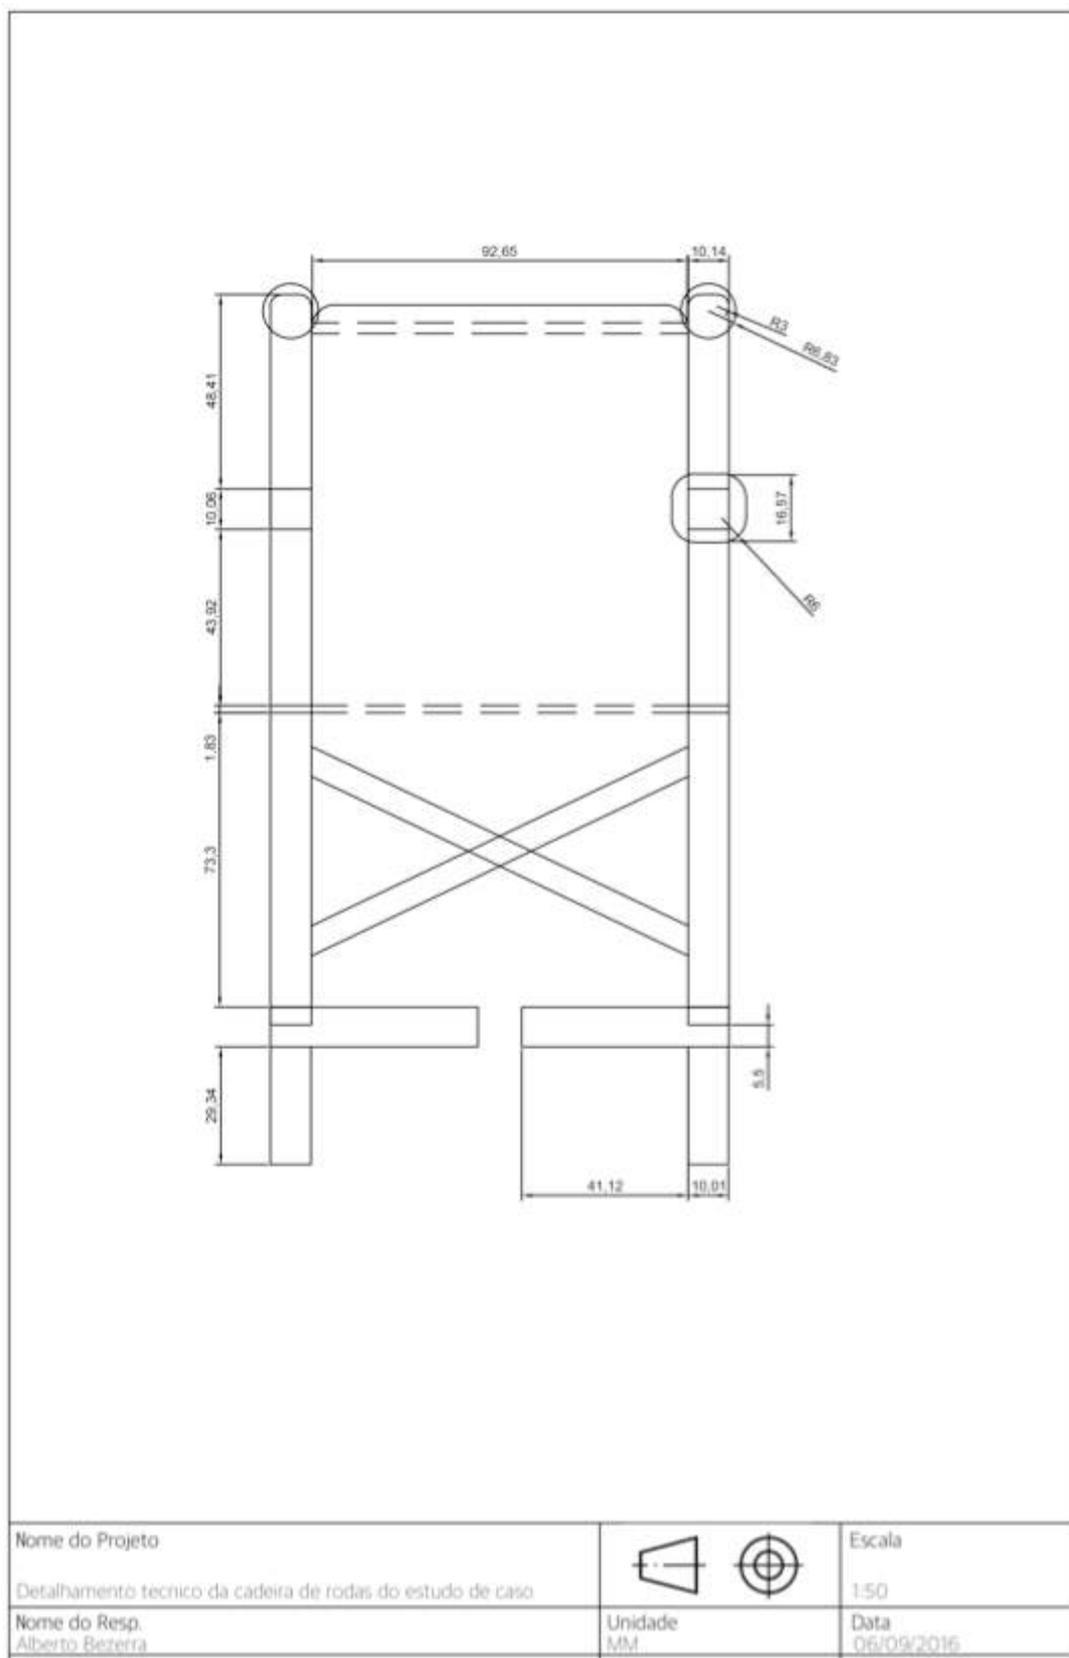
Vista frontal da cadeira de roda - Fonte: o autor
